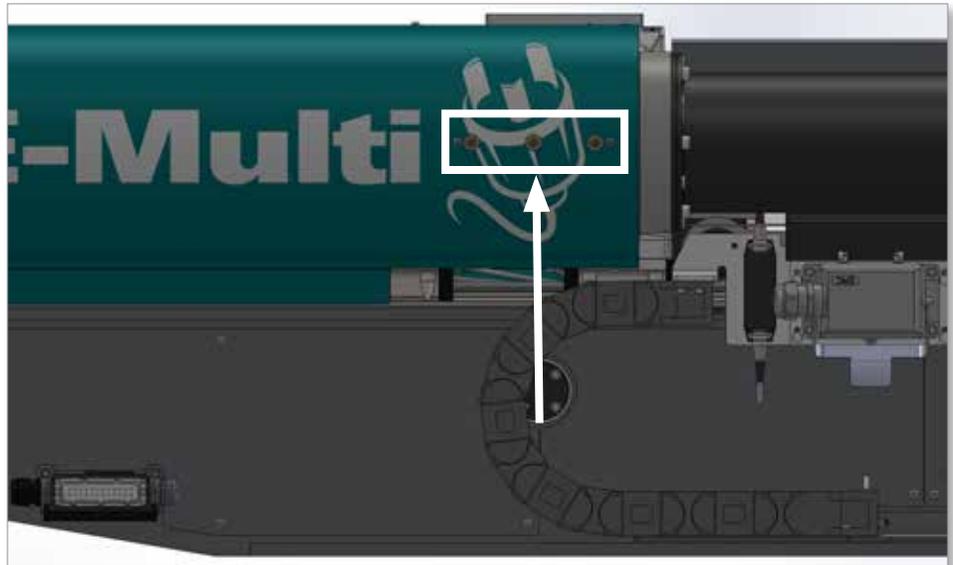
Seitenansicht mit den Schmierpunkten der Kugelgewindespindel (insgesamt 6; 3 auf der anderen Seite)
